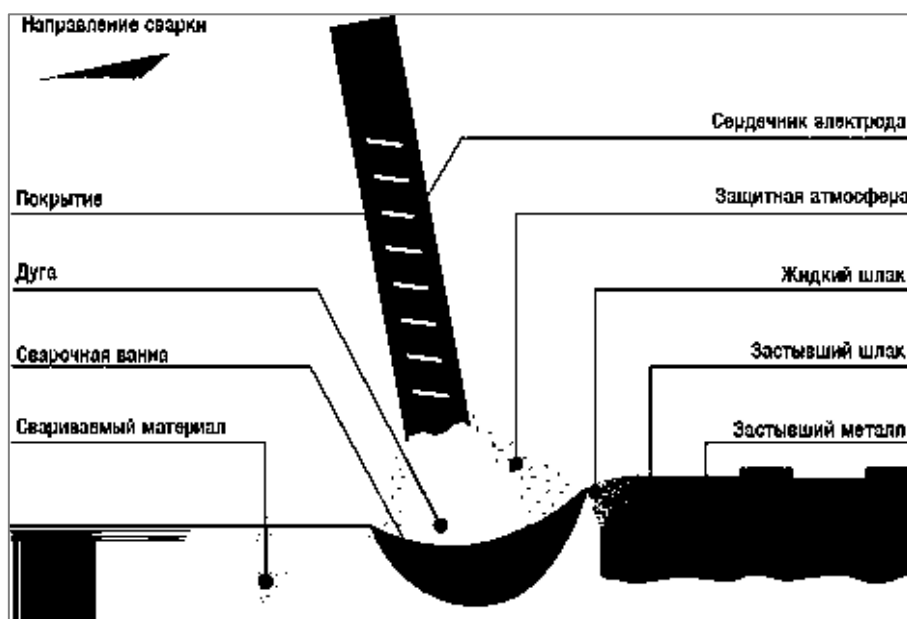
Процесс ручной дуговой сварки
